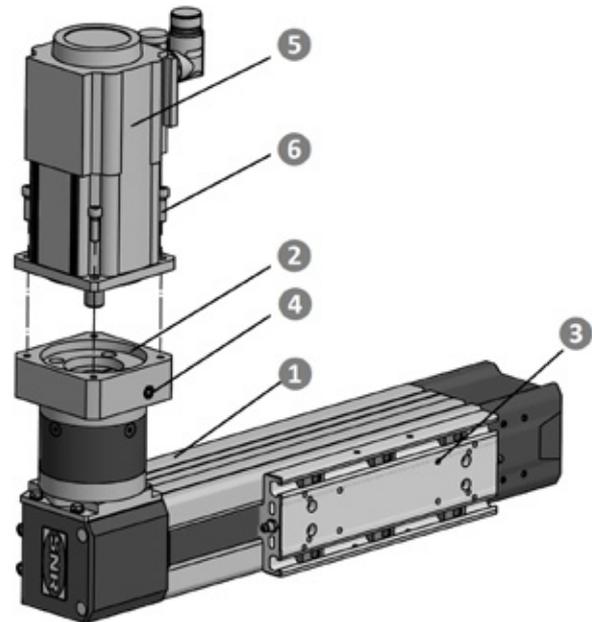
Motormontage an Linearachsen Planetengetriebe
